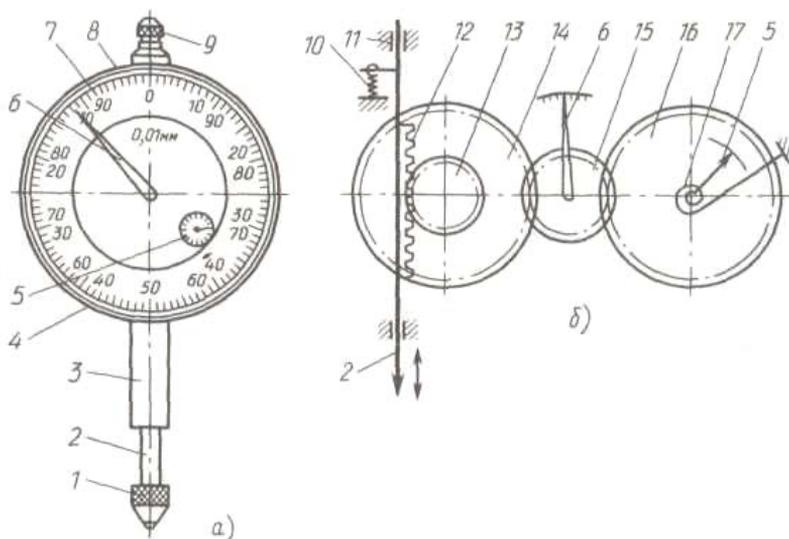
Индикатор часового типа: а) общий вид; б) схема прибора
